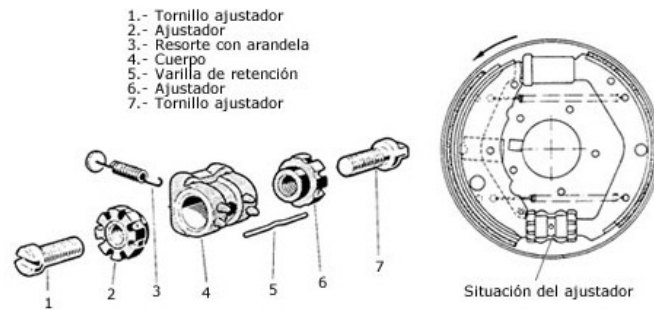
Diagrama de explosión del conjunto ajustador [6].
